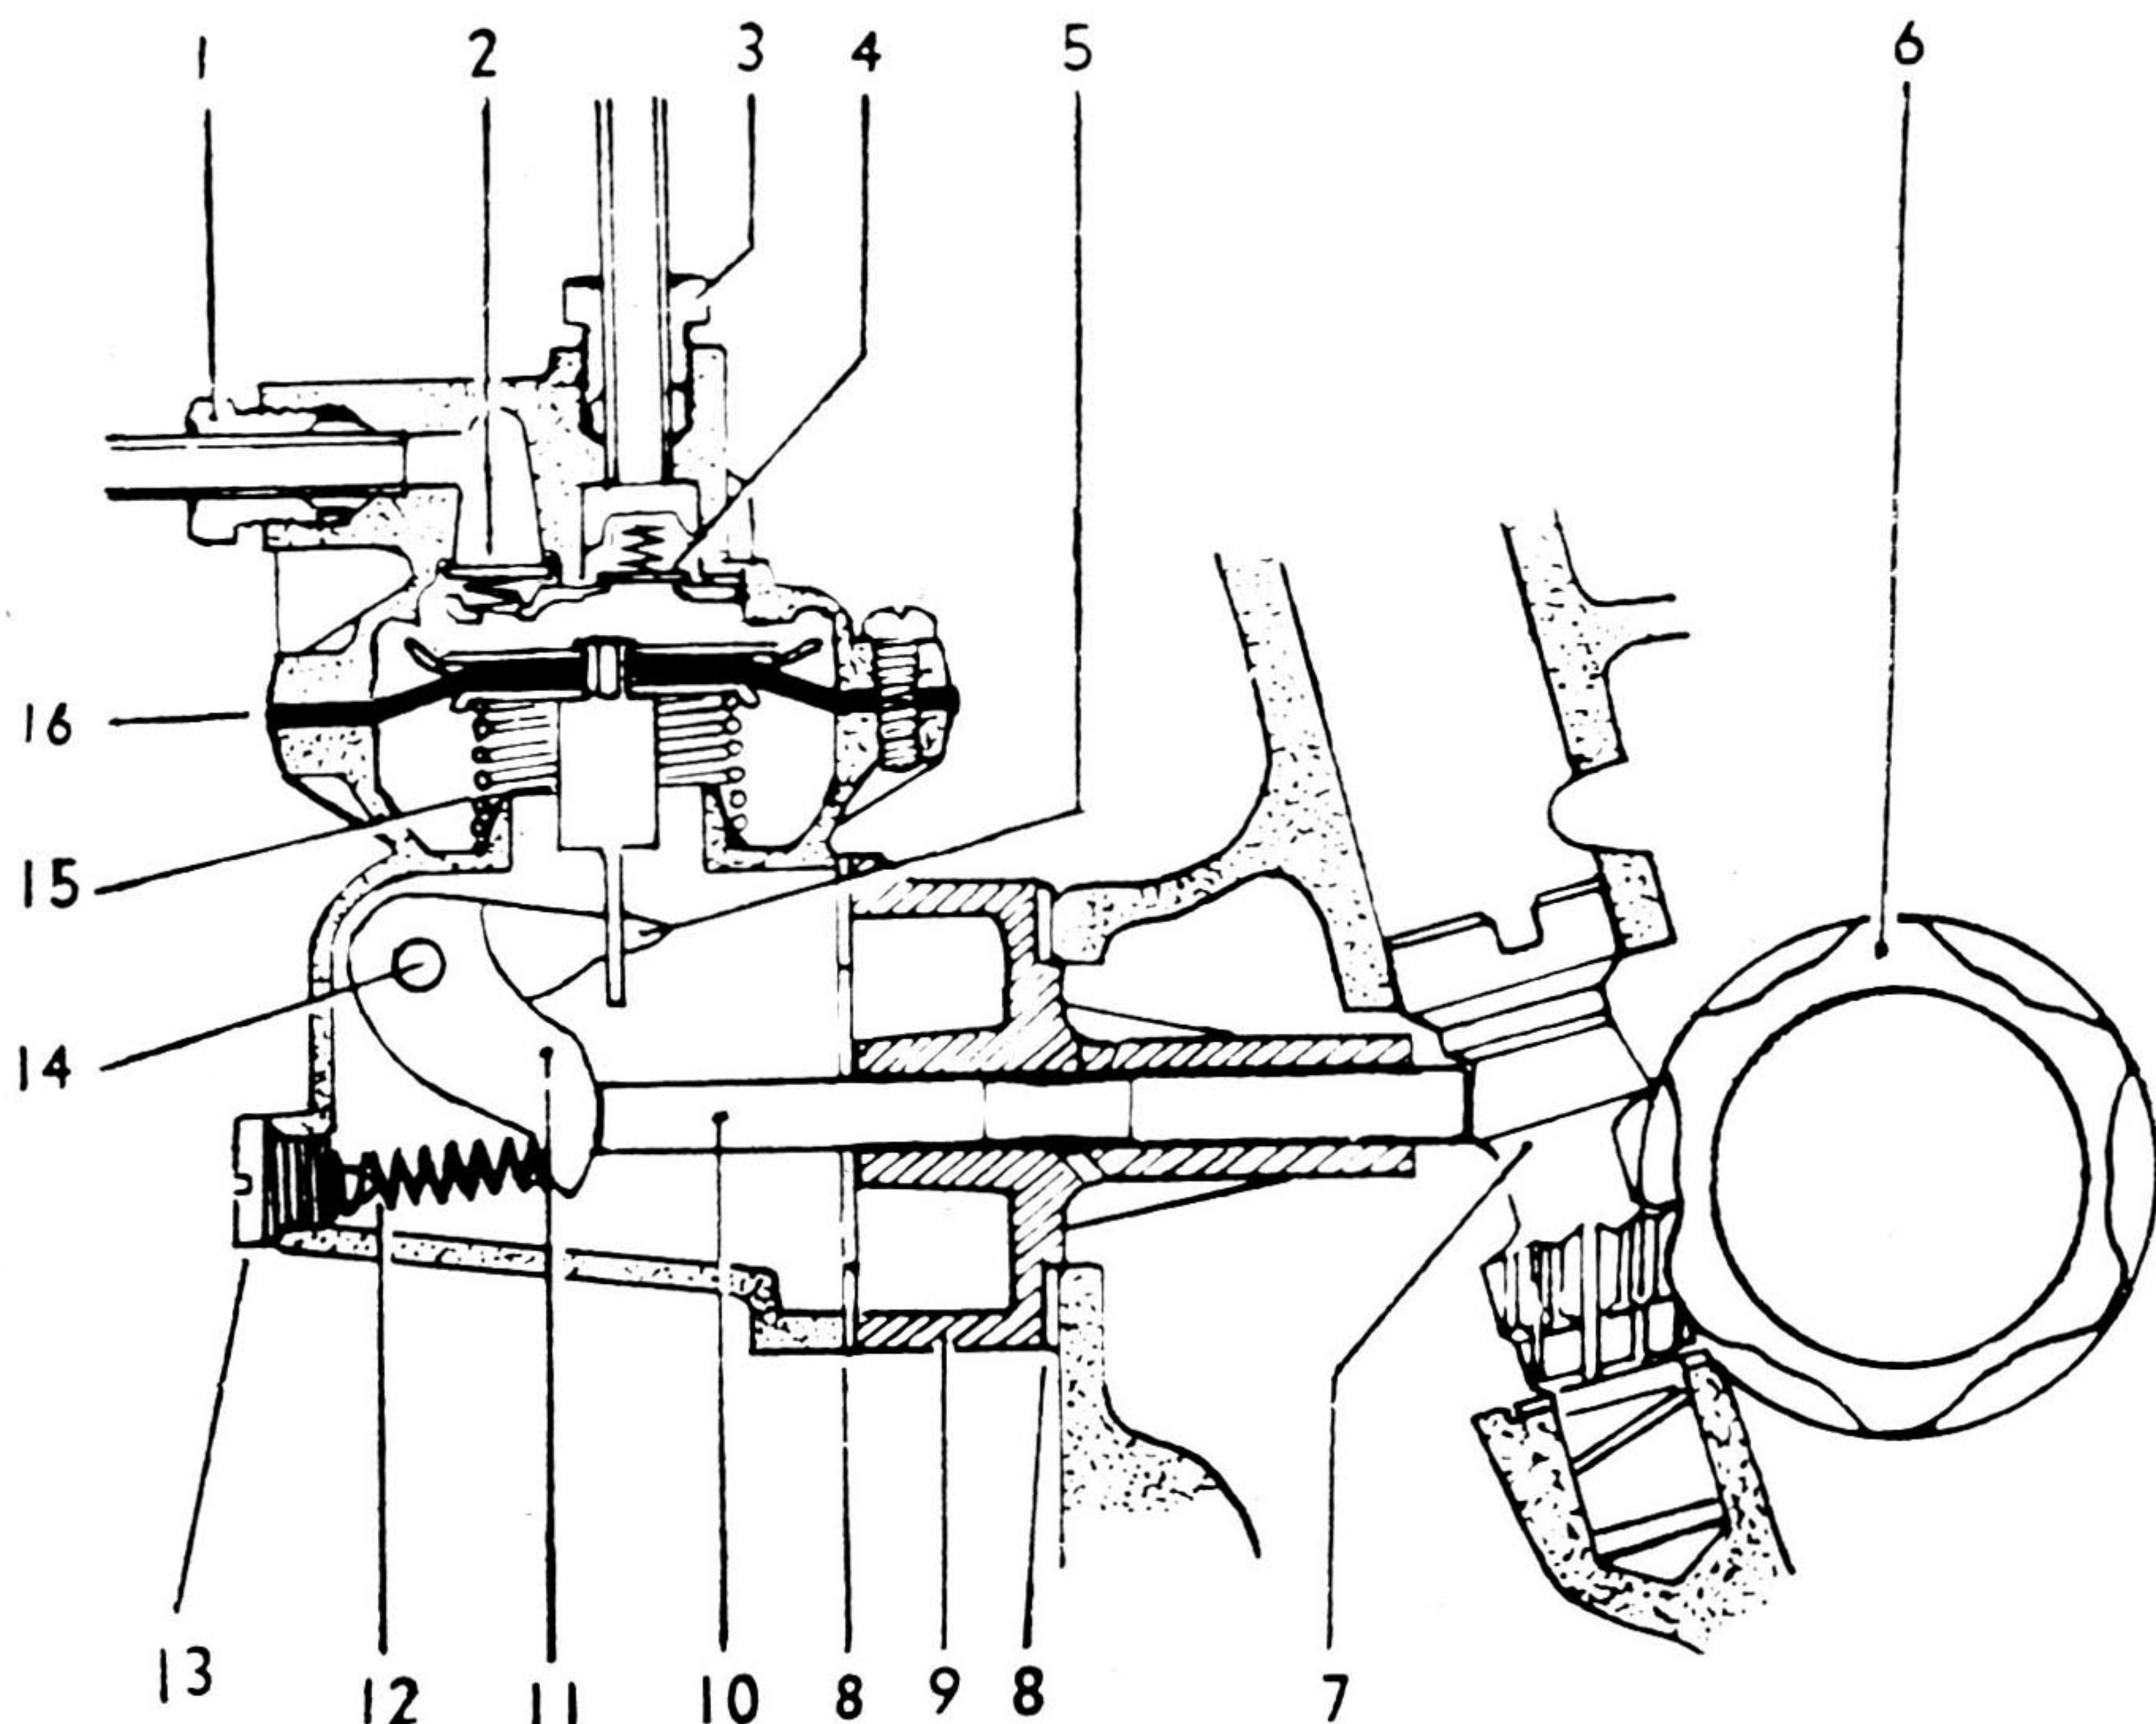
E — Corte da bomba de gasolina. (Motor “1 200” — 36 HP)
